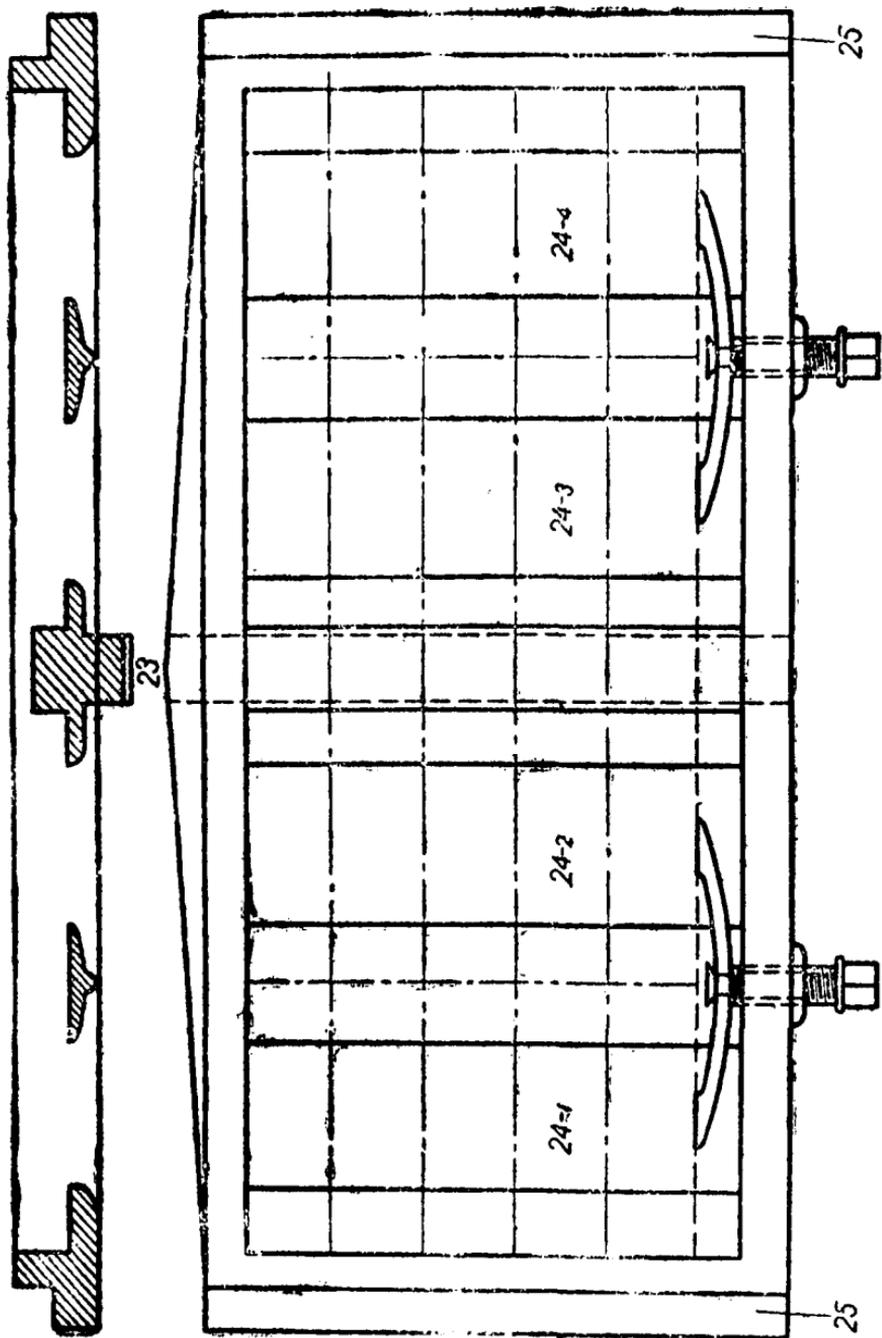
Проект станка т. Пурецкого. Приспособление для зажима болтов при операциях 1-й, 4-й и 5-й: 23—зубчатая рейка; 24—ряды зажатых планок; 25—места, которыми приспособление вставляется в пазы станины.
